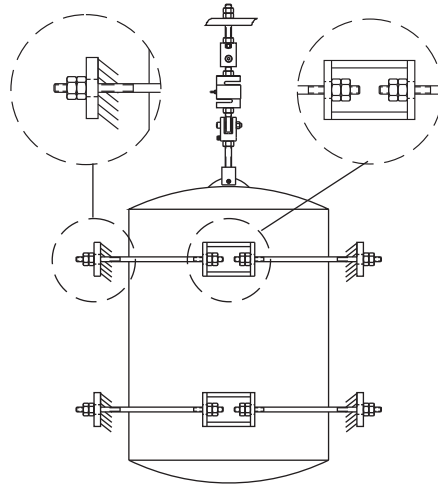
Aplicaciones de Barras Estabilizadoras
